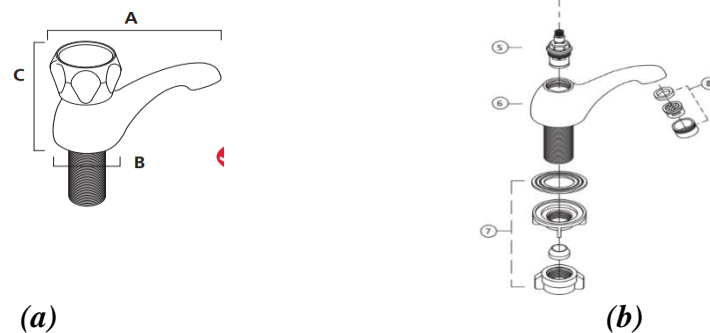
grifería – Shelby, (a) vista lateral, (b) vista explosionada [23]
